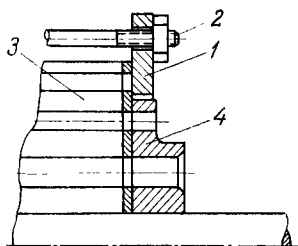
Установка приспособлений для стяжки пакета активной стали ротора при демонтаже нажимных шайб.
